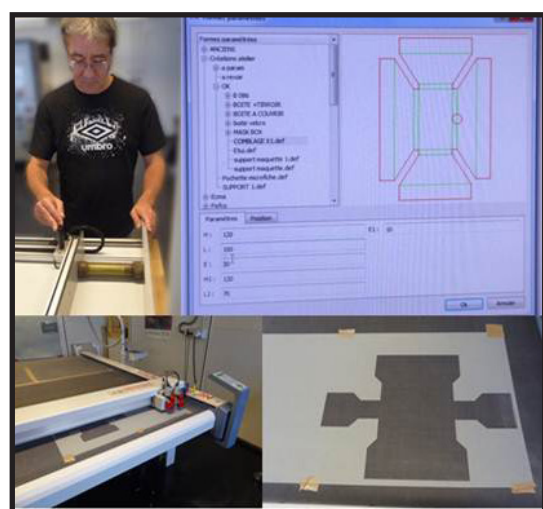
(A) mesures des cylindres, (B) création du gabarit de découpe, (C) table de découpe, (D) carton découpé.
